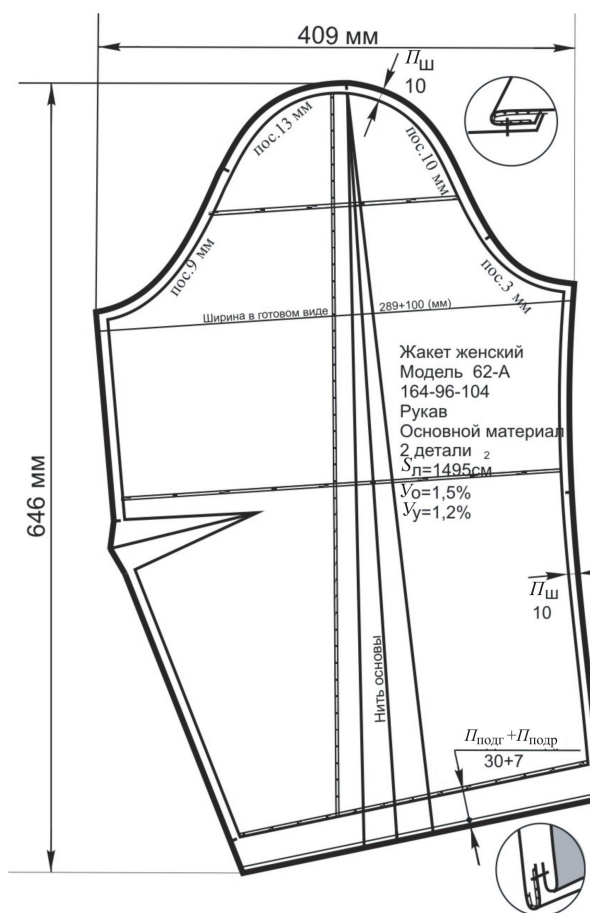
Рабочий чертеж лекала рукава женского жакета
